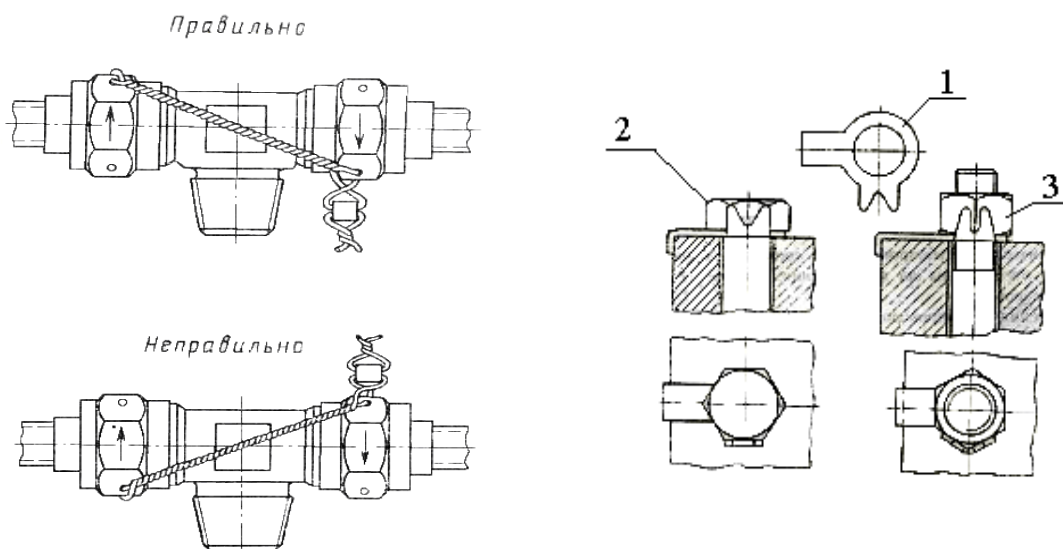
Контровка проволокой Рис. 3.7. Контровка стопорной шайбой с лапкой:
